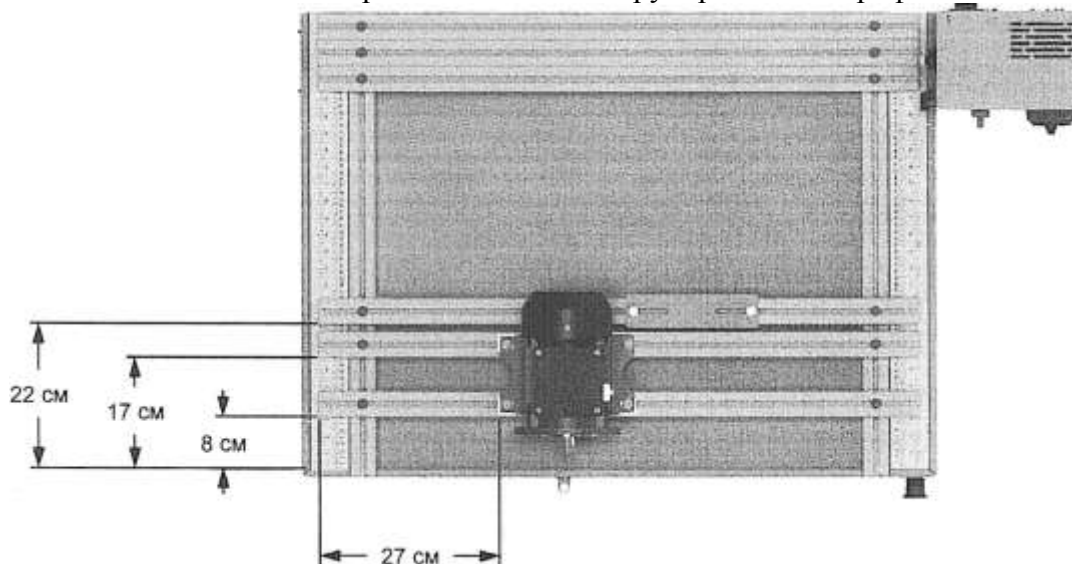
Схема рабочей станции для коррекции неплотно прилегающей опоры.
